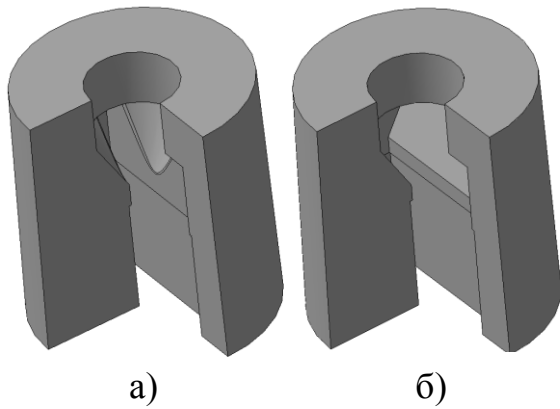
Матриці для видавлювання з роздачею: а)- конічна, б)- призматична.
